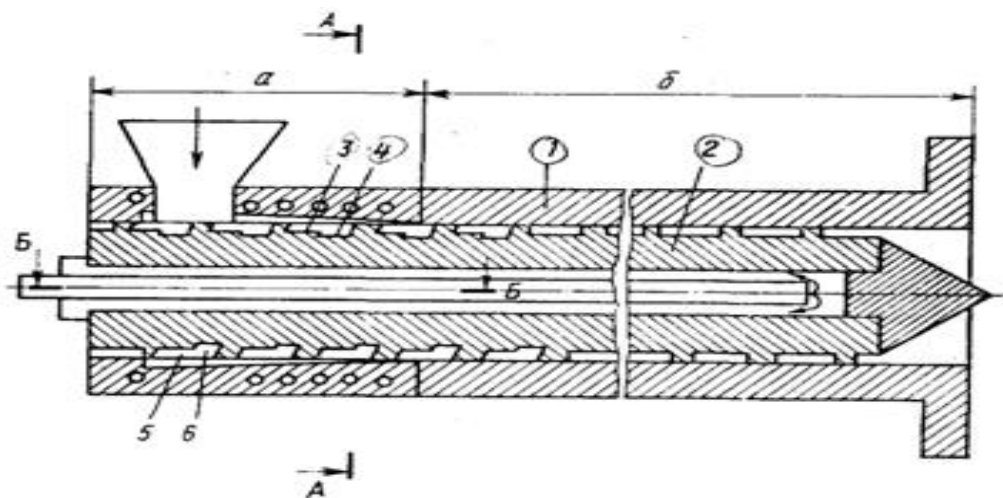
Пристрій для підготовки та змішування.
